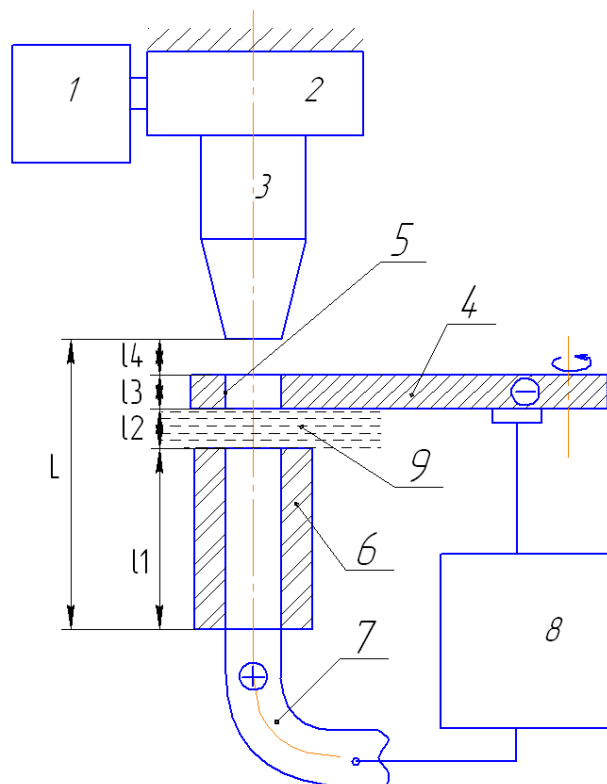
Схема комбинированного удаления технологической вставки из минералокерамической втулки:
